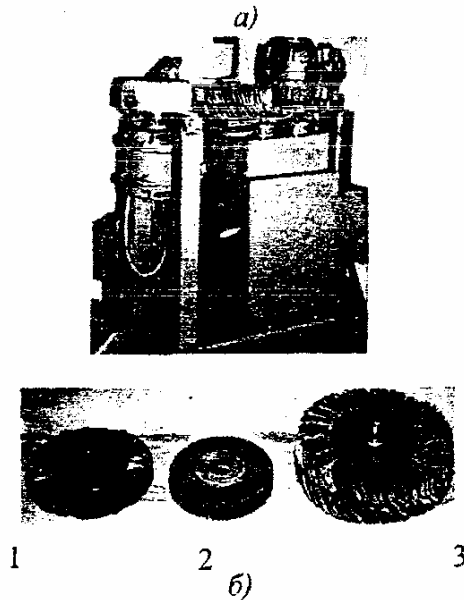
Установка для абразивной обработки цилиндрической поверхности детали (а) и абразивный и лезвийный инструмент (б): 1 - иглофреза; 2, 3 - лепестковые круги
